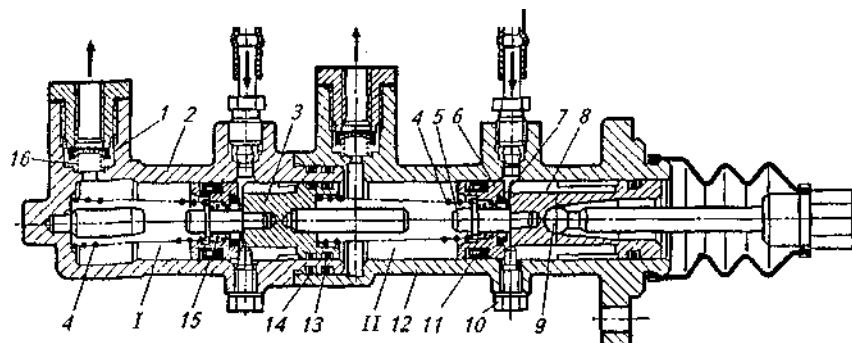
Главный тормозной цилиндр автомобилей ГАЗ: I, II— полости главного тормозного цилиндра; 1 — клапан избыточного давления; 2, 12— соответственно вторичный и первичный картеры; 3, 8 — соответственно вторичный и первичный поршни; 4— возвратные пружины поршня; 5—упорный стержень; 6— головка поршня; 7— уплотнительное торцевое кольцо; 9— толкатель; 10 — упорный болт; 11 — манжета; 13, 14 — соответственно уплотнительные кольца поршня и корпуса; 15 — пружина головки поршня; 16— пружина клапана избыточного давления
